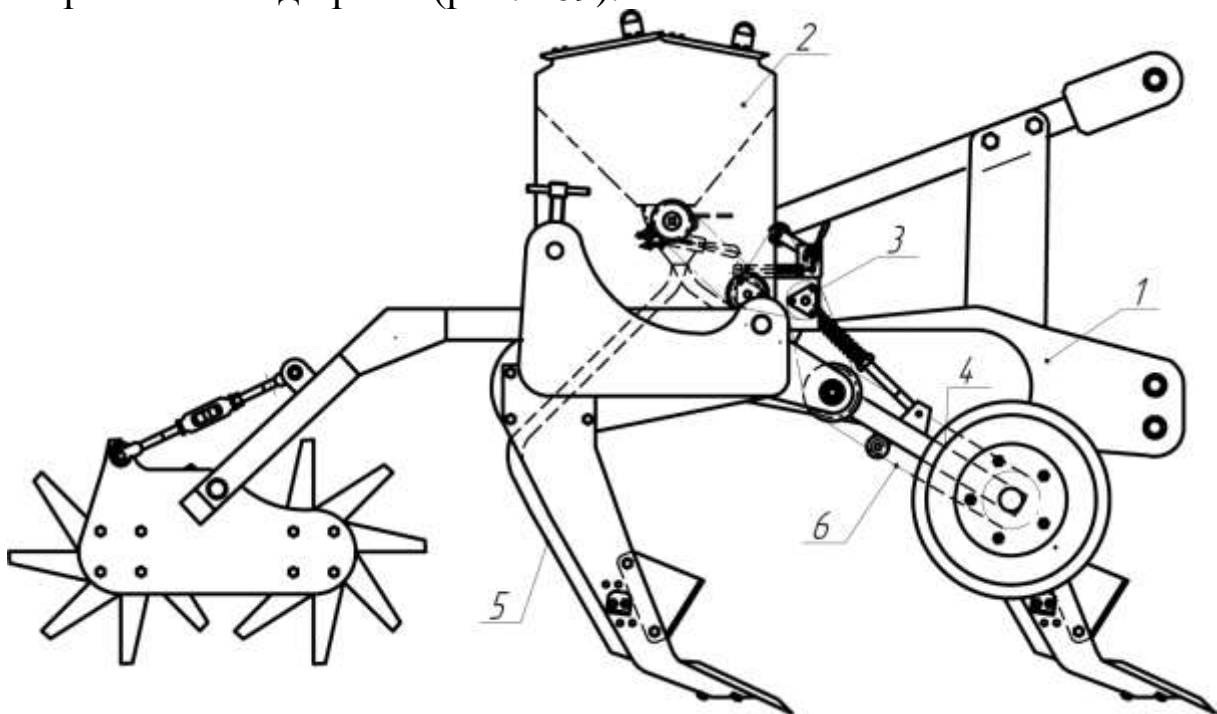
Загальний вигляд глибокорозпушувача-удобрювача:
